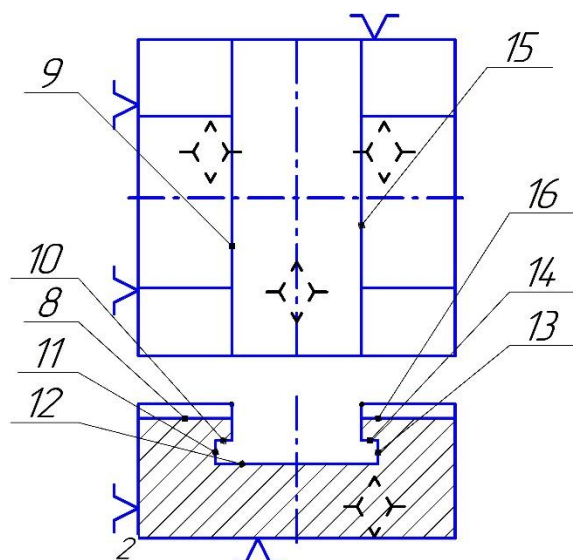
Поверхности для фрезерования с ЧПУ
